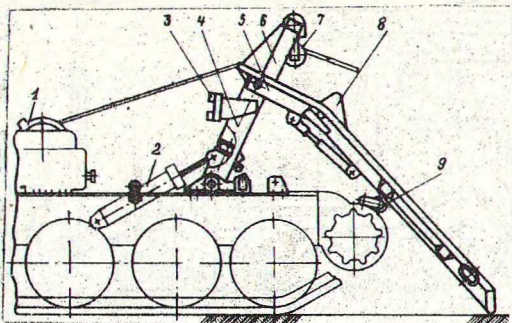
Погрузочное устройство гусеничного трелевочного трактора: 1-лебедка; 2-гидроцилиндры; 3-буфер; 4-поворотная рамка; 5-плит; 6-щека; 7-блок; 8-отражатель; 9-ролик.
